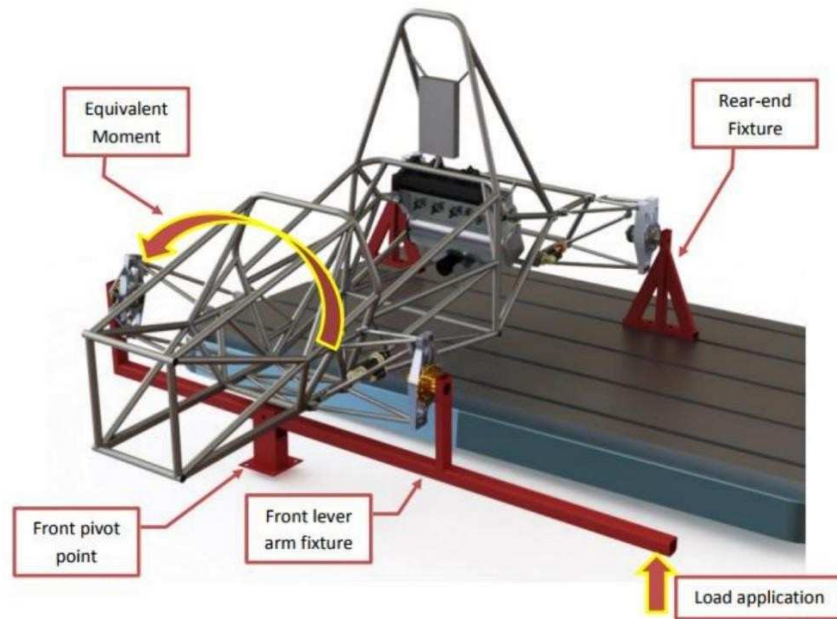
Gabarit d'assemblage des cadres BUGGY.
